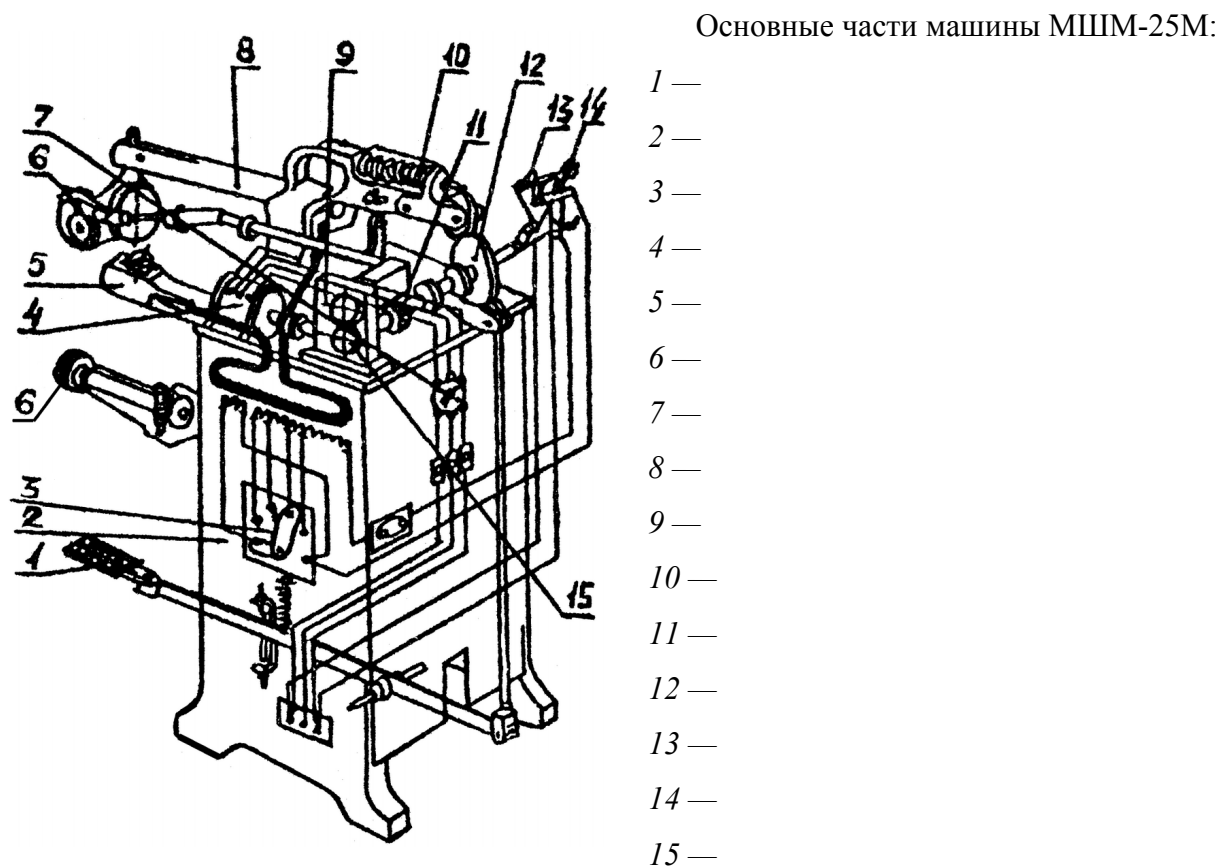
Схема машины для контактной шовной сварки МШМ-25М
